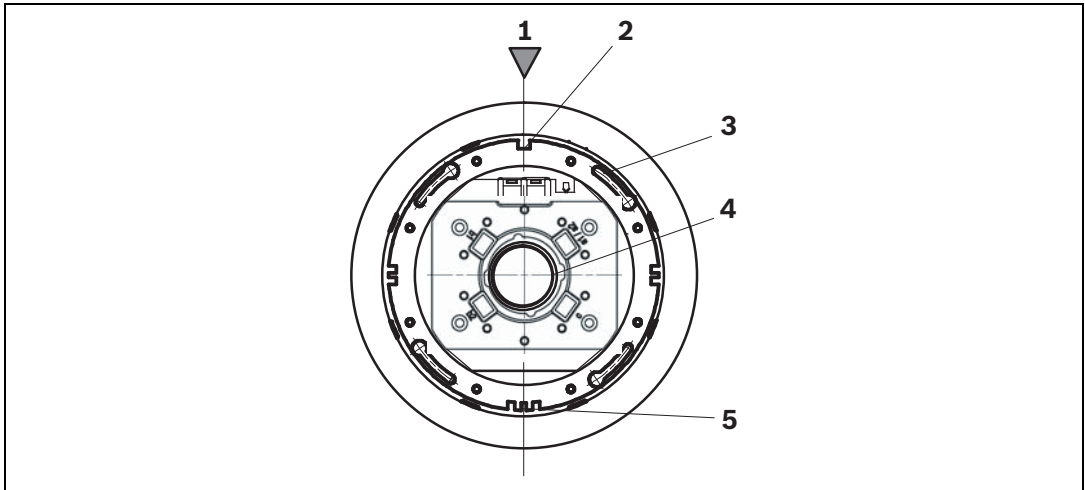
Fixation du socle au boîtier arrière pour montage au plafond
